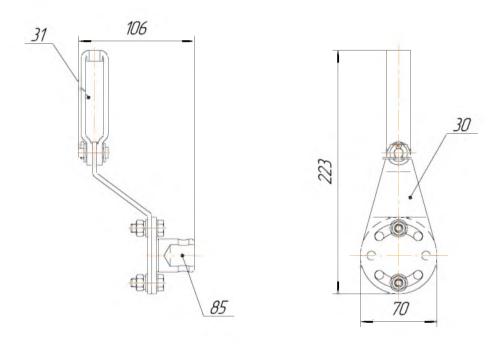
Рычаг для управления приводов заземлителя разъединителя 30 – рычаг; 31 – серьга; 85 – втулка
